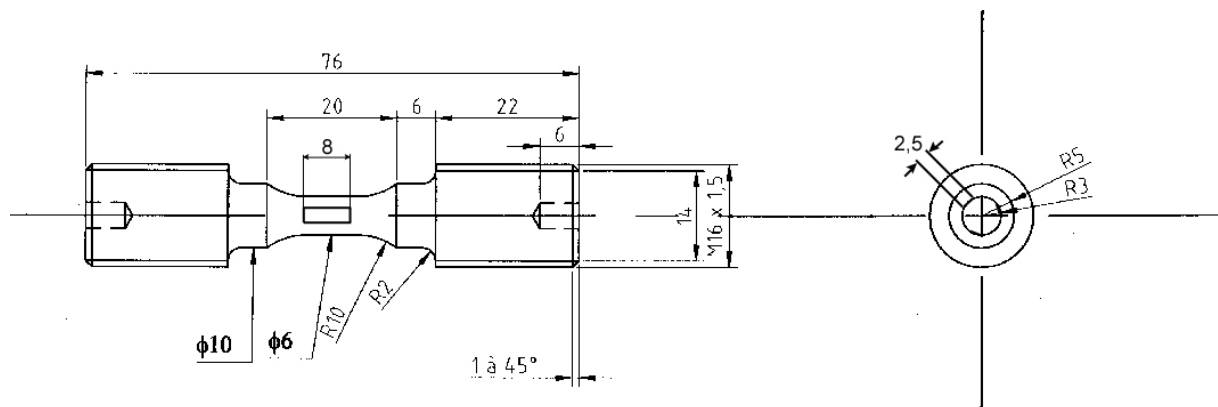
Forme et dimensions des éprouvettes de fatigue oligocyclique avec méplats
